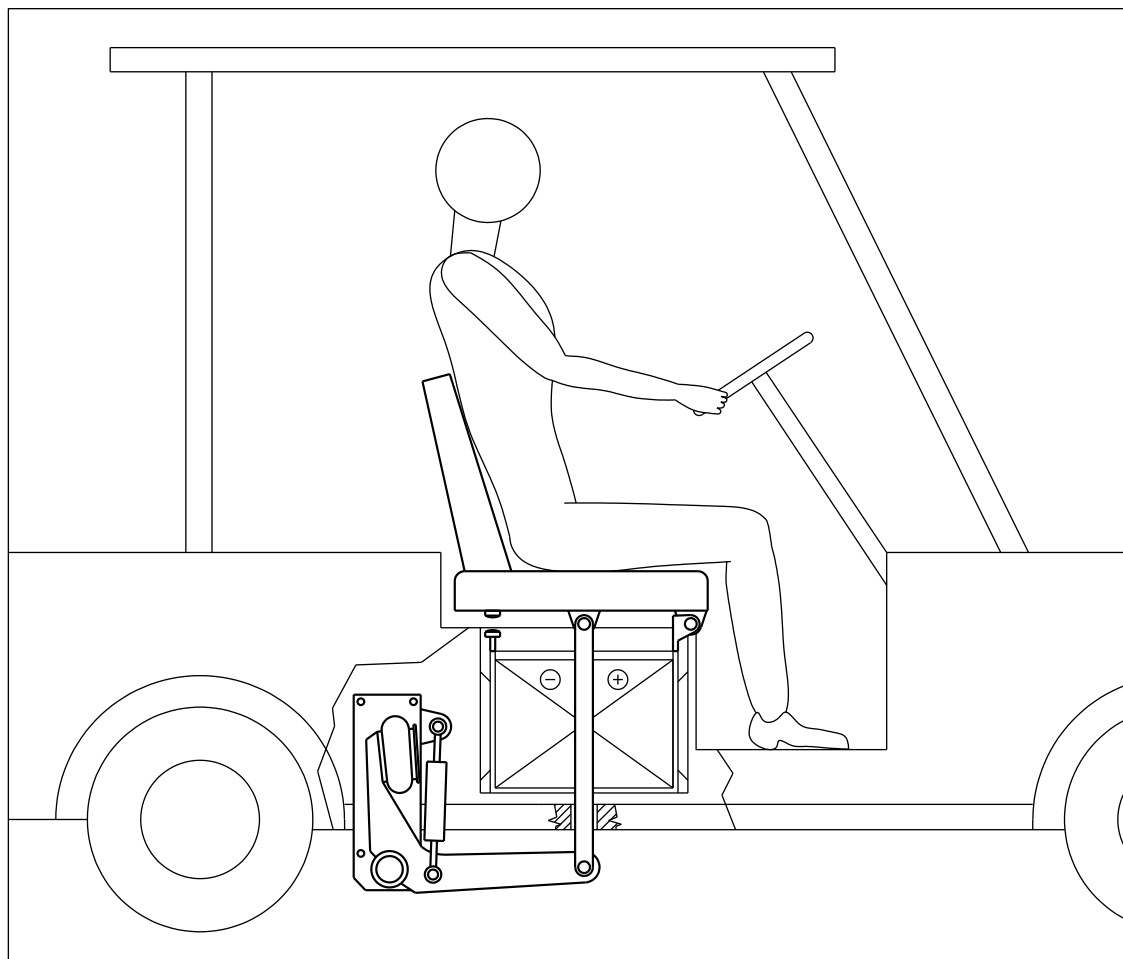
Konstrukční varianta 3 – odpružení sedadla a baterie
